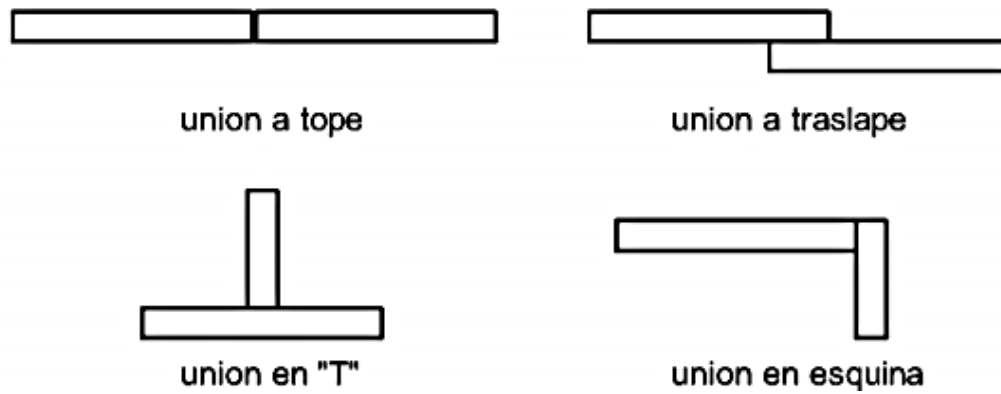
Diseños de uniones soldadas más comunes
